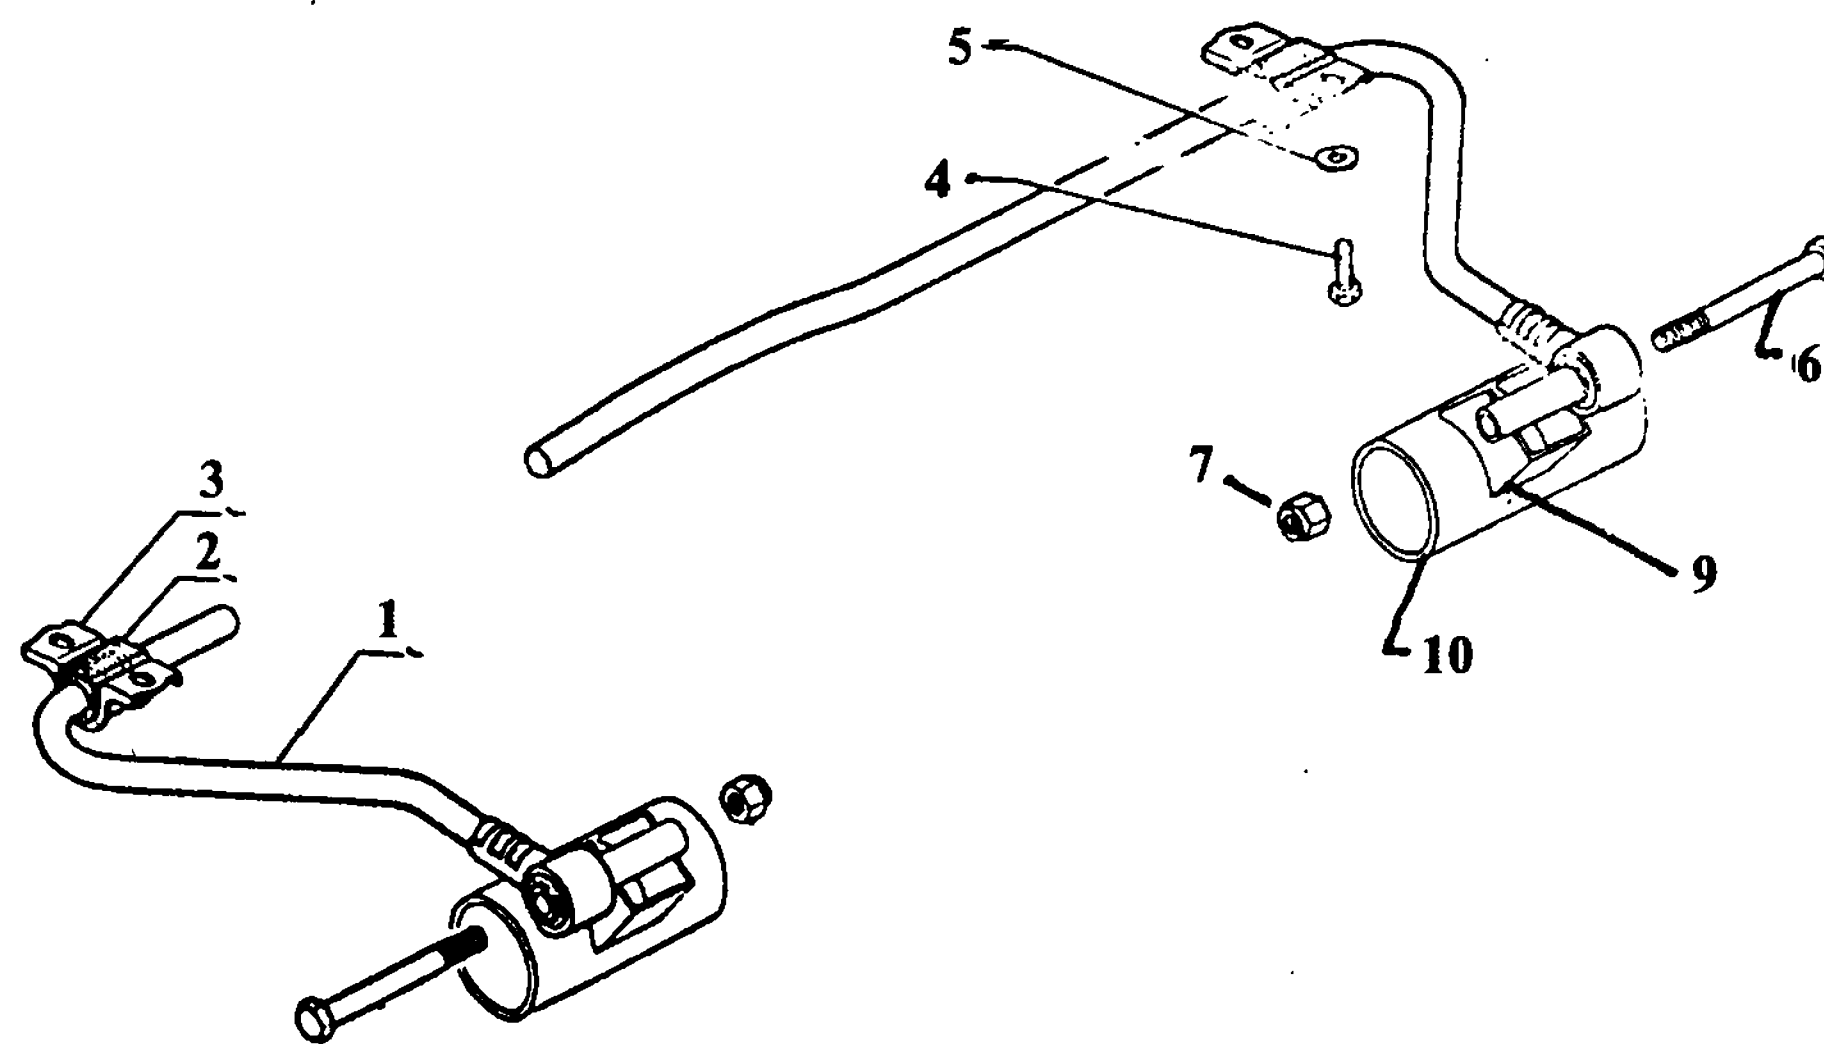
Установка стабилизатора заднего моста: 1 - штанга стабилизатора с сайлентблоками в сборе; 2 - подушка штанги; 3 - скоба крепления подушки; 4 - болт крепления скобы; 5 - шайба пружинная; 6 - болт крепления штанги стабилизатора к кронштейну заднего моста; 7 - гайка болта; 9 - приварной кронштейн заднего моста; 10 - балка заднего моста
